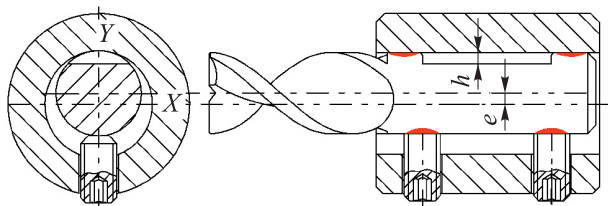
Схема инструментального блока со втулкой конструкции Weldon (h — высота уступа площадки на хвостовике фрезы)
